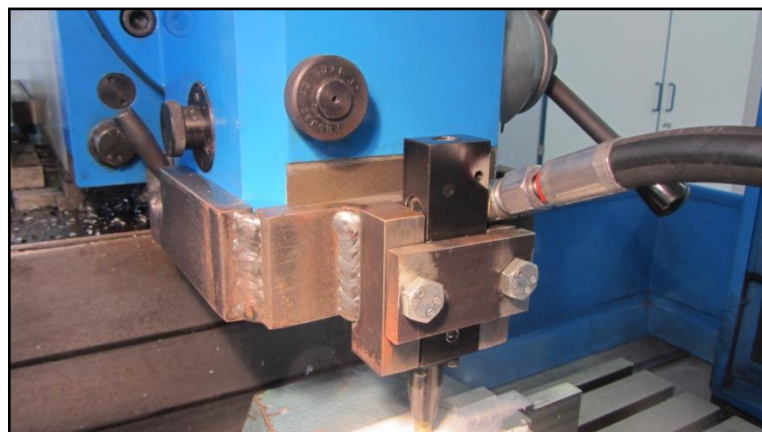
Montage des Festwalzwerkzeuges und des Hydraulikschlauches
